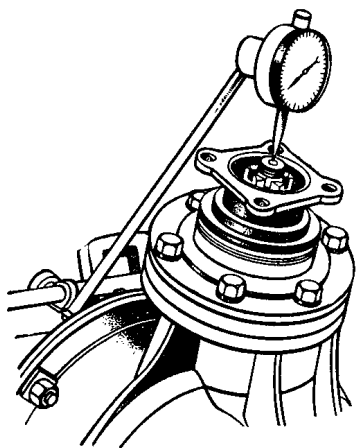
Проверка осевого зазора в подшипниках вала ведущей шестерни главной передачи
